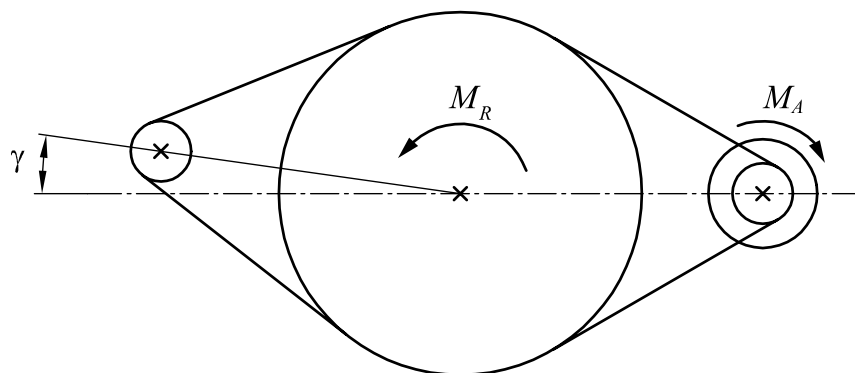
Skizze des Riemenantriebs mit Hilfsrad
